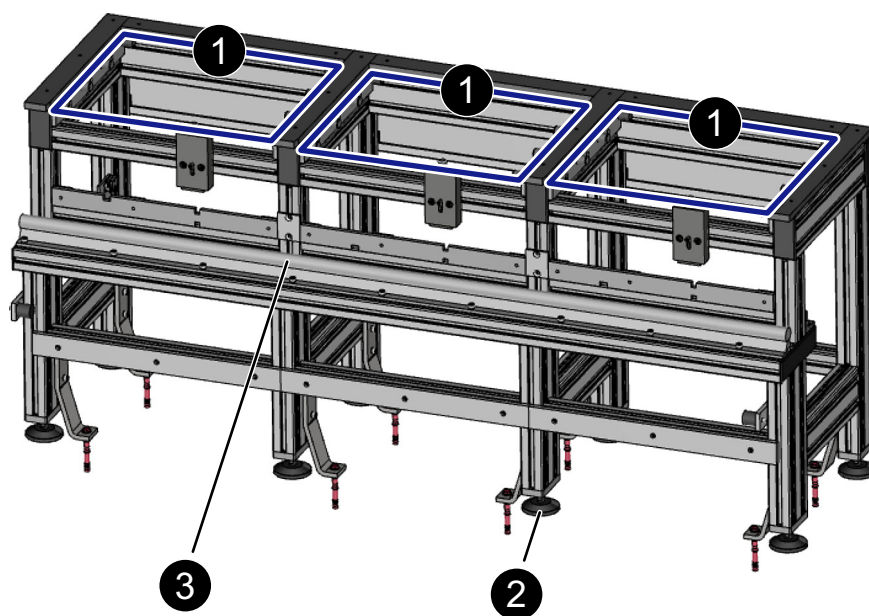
Stazione navetta longitudinale (figura esemplificativa)
